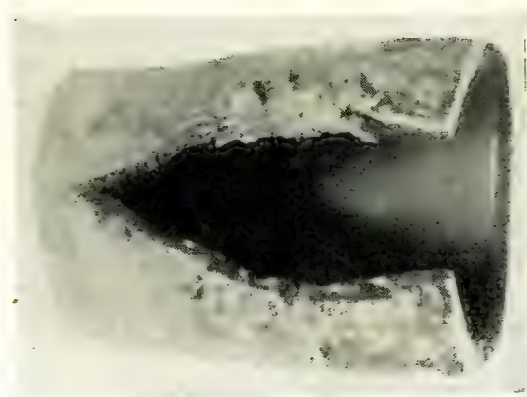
Разрыв трубы пароперегревателя, изготовленной из стали марки 15ХМ.
